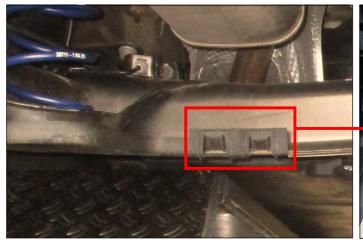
& 6: Ausklinken des Steinschlagschutzes (fahrzeuginnere Klemmbefestigung wird entfernt)
